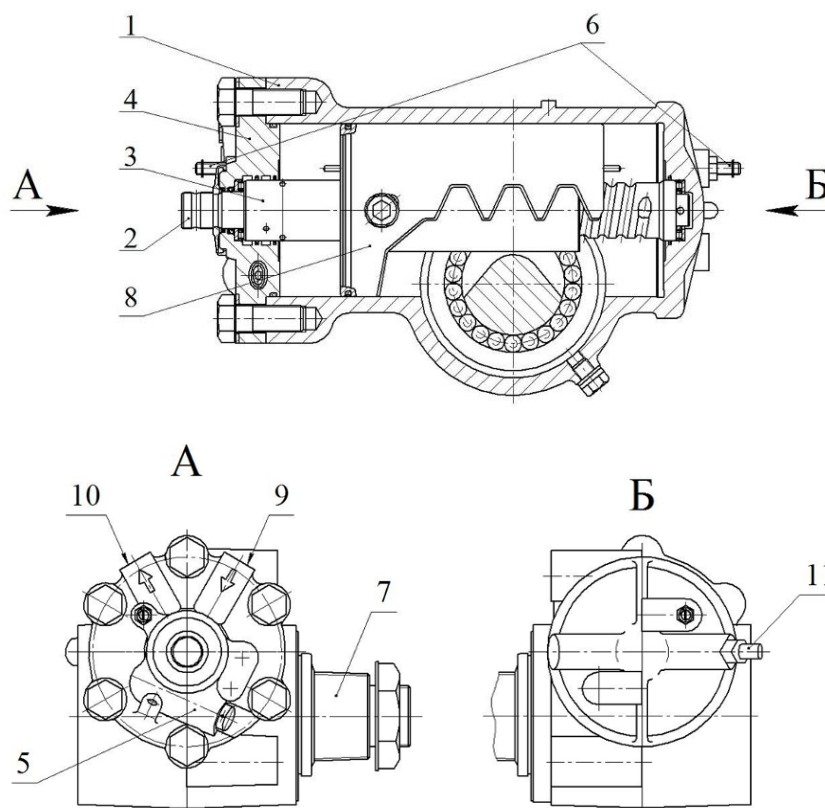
Загальна будова гідравлічного підсилювача ШВГУ 720: 1 – картер пристрою; 2 – ротор; 3 – гвинт; 4 – корпус розподільника; 5 – порожнина під запобіжний клапан; 6 – упори кінцевих вимикачів; 7 – вал сошки; 8 – рейка-поршень; 9 – напірна магістраль; 10 – зливна магістраль; 11 – клапан для видалення повітря.
